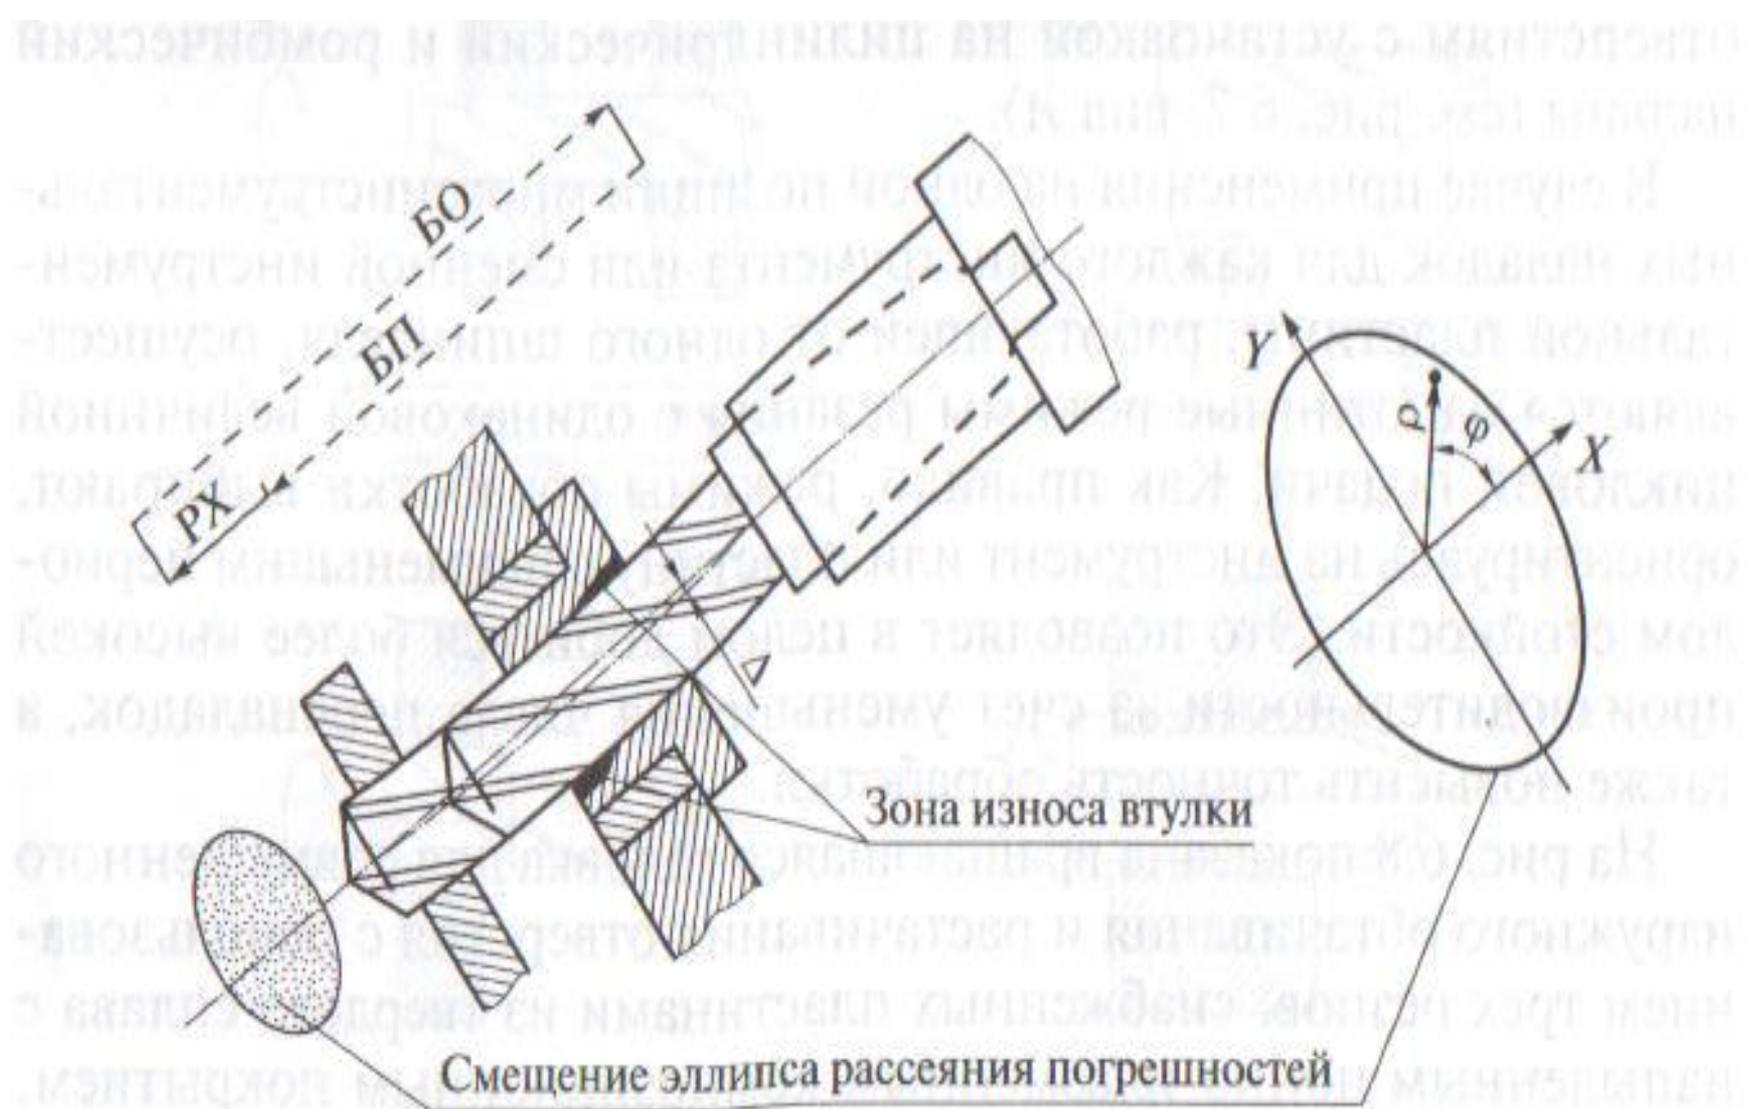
Поле рассеяния положения сверла при несовпадении осей шпиндельной головки и кондукторной втулки
